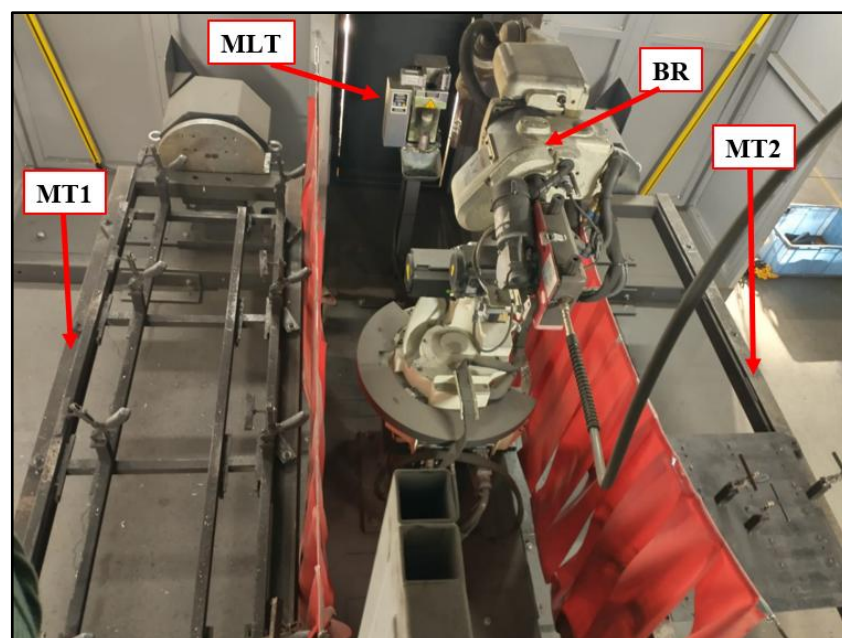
Braço Robótico de Solda e Mesa de Trabalho.
